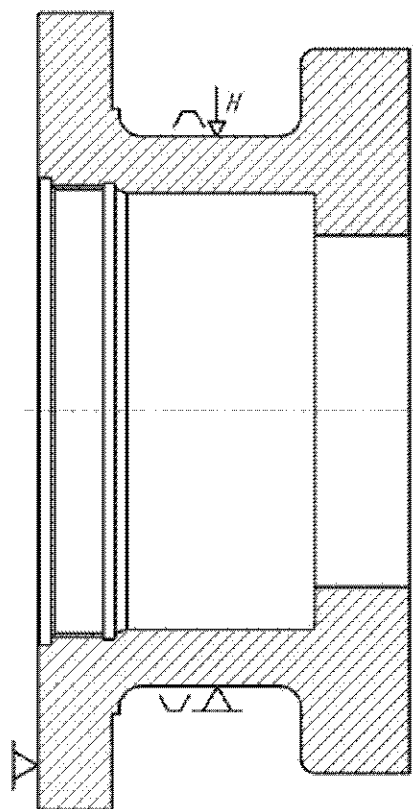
Схема базирования заготовки на операции 005 комплексная на обрабатывающих центрах с ЧПУ (установ Б)
